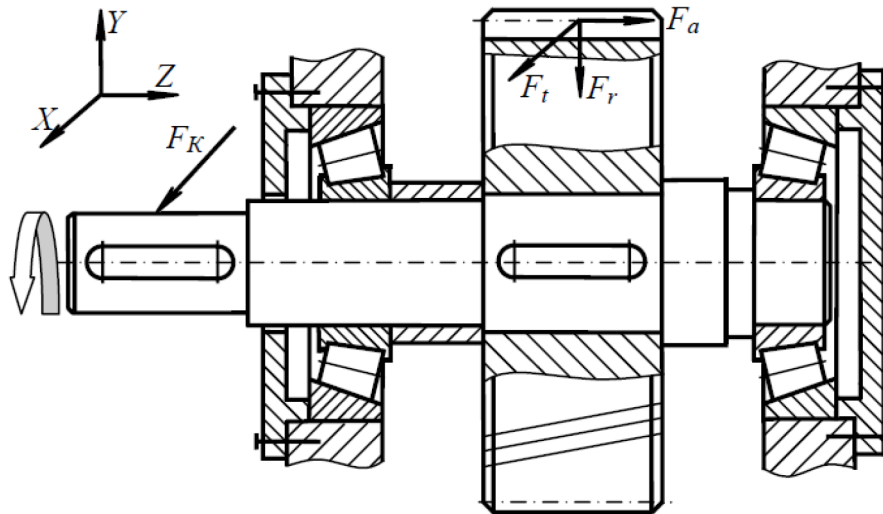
Установка роликовых конических однорядных подшипников по схеме враспор на ведомом валу цилиндрического косозубого редуктора
